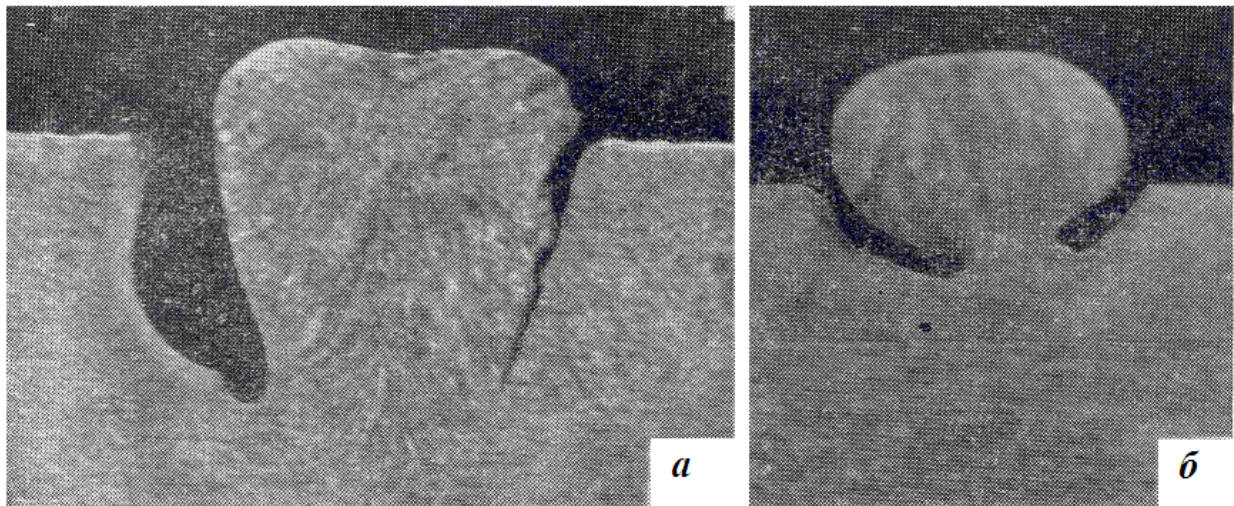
Зона несплавления при дуговой сварке
